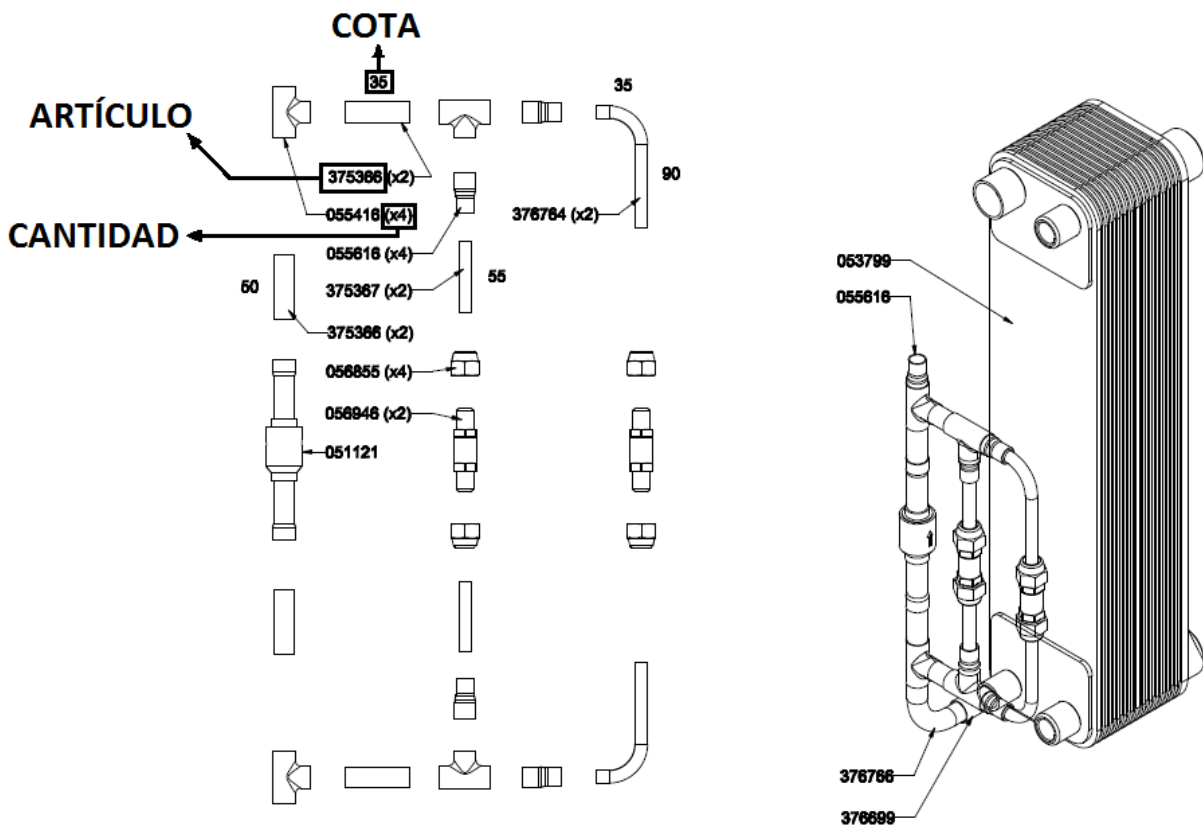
Explosionado de una araña de la máquina WPHBA 1001 y su montaje en el intercambiador de placas.
